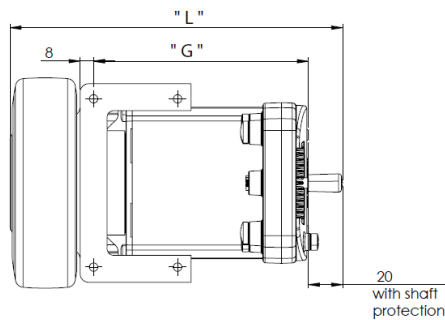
Dimensions hors tout – 'SWD® 125 2-stages'
